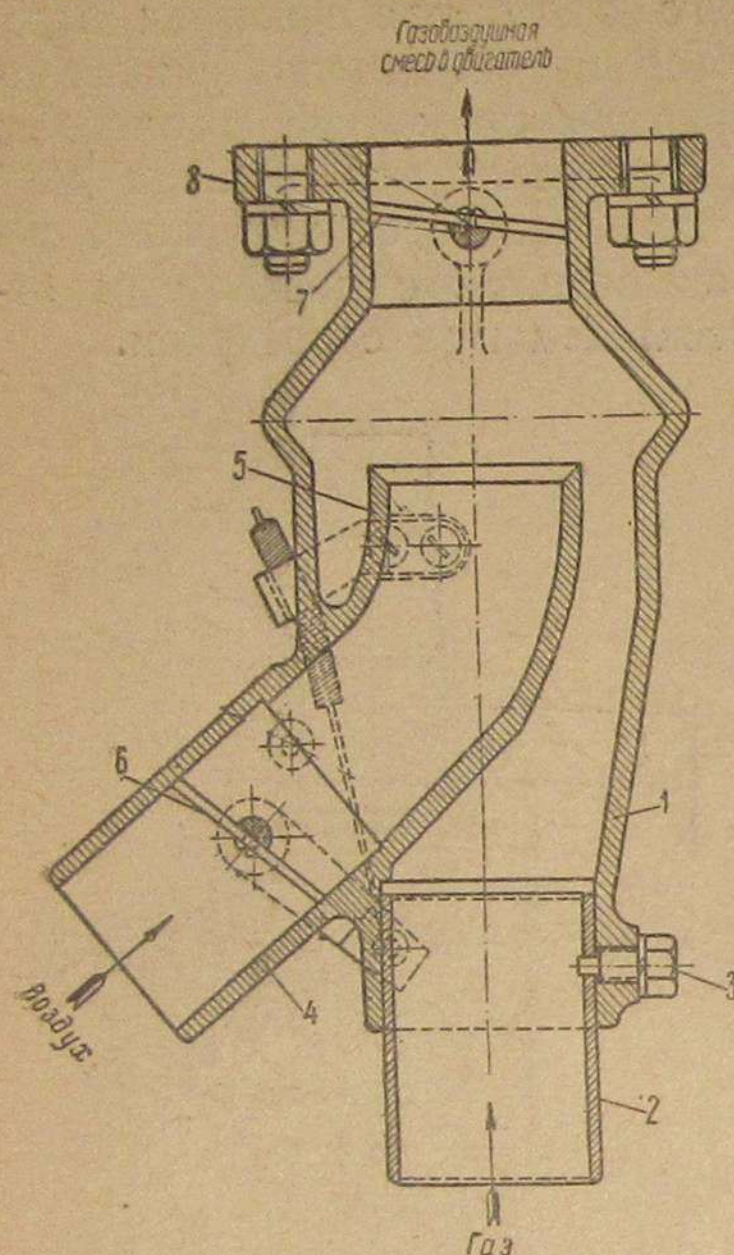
Смеситель газа с воздухом установки ЗИС-21:
